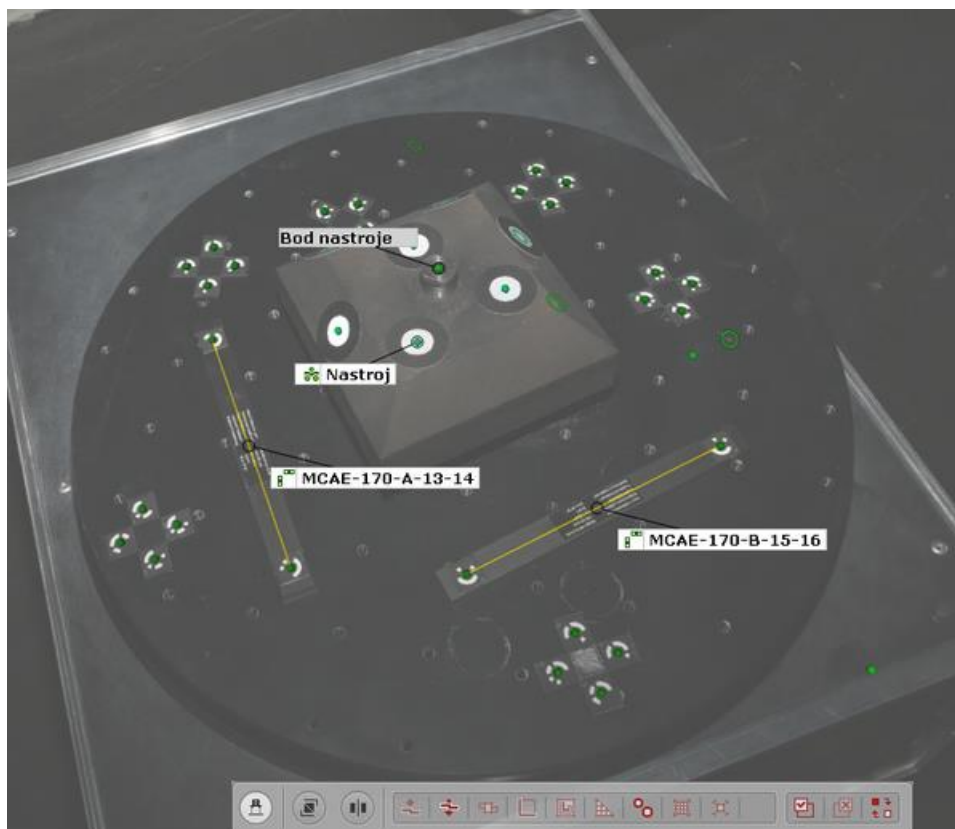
Mechanický upínač s nosným prvkem, detailní pohled.
